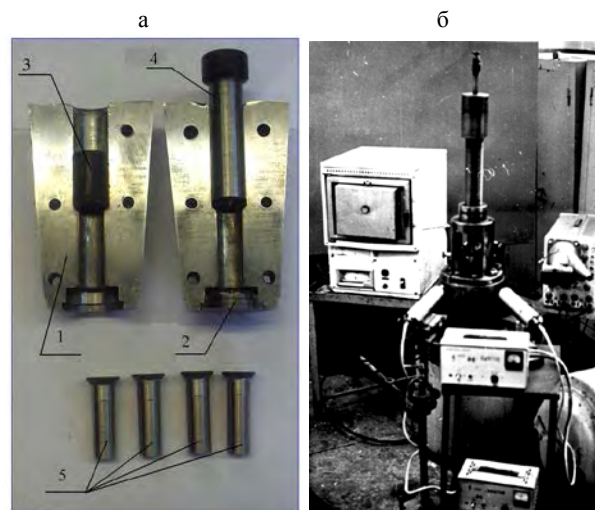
а – внешний вид технологической оснастки для реализации процесса СГВ с ПТЧ пуансонов штампов для холодной пробивки отверстий: 1 – полуматрица; 2 – матричная вставка; 3 – заготовка; 4 – ударник; 5 – готовые изделия; б – то же экспериментальной установки с пороховым приводом
